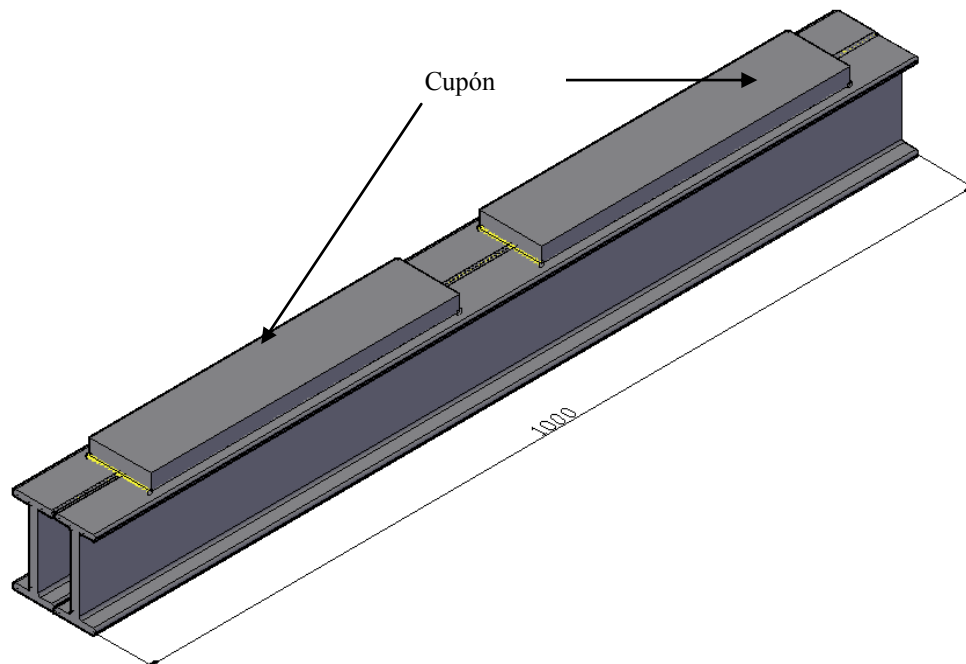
4. Conjunto cupón - dispositivo rigidizador (dimensiones en mm).
